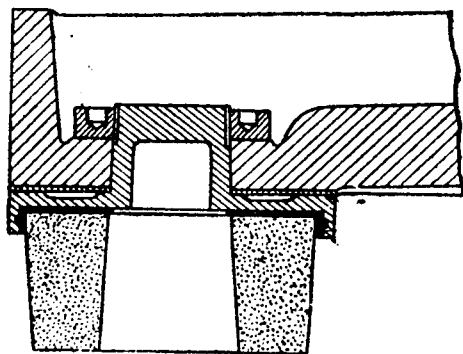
Конструкция оправки для крепления сегмента на планшайбе шлифовального станка „Дискус“
